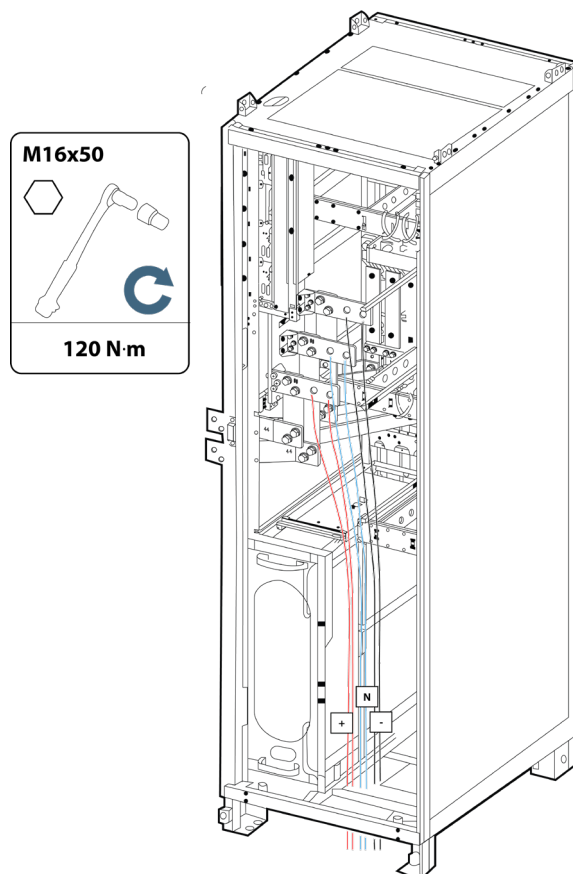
CABLEADO DE CONEXIÓN DEL BANCO DE BATERÍAS AL UPS.
